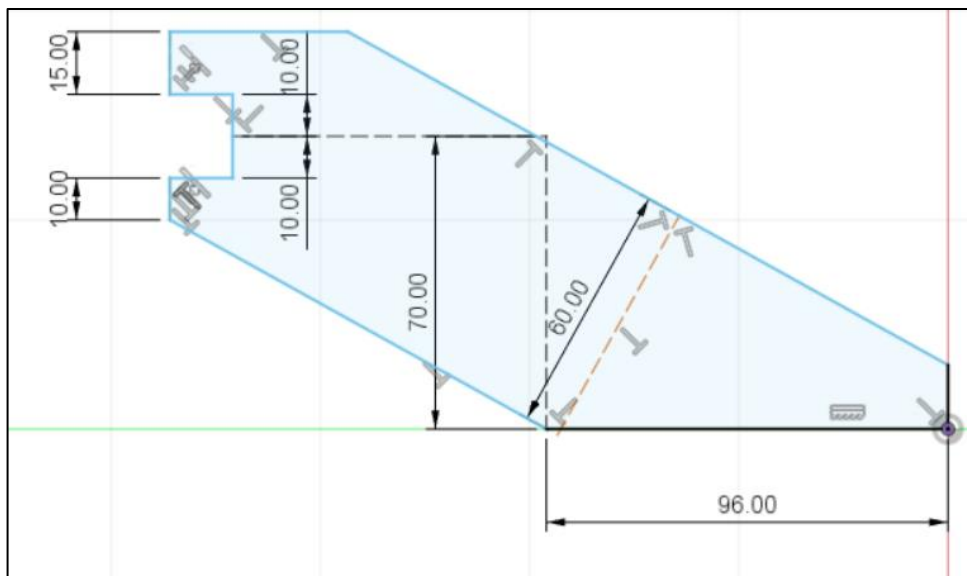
Эскиз детали 7: опора направляющей (2 шт.)
